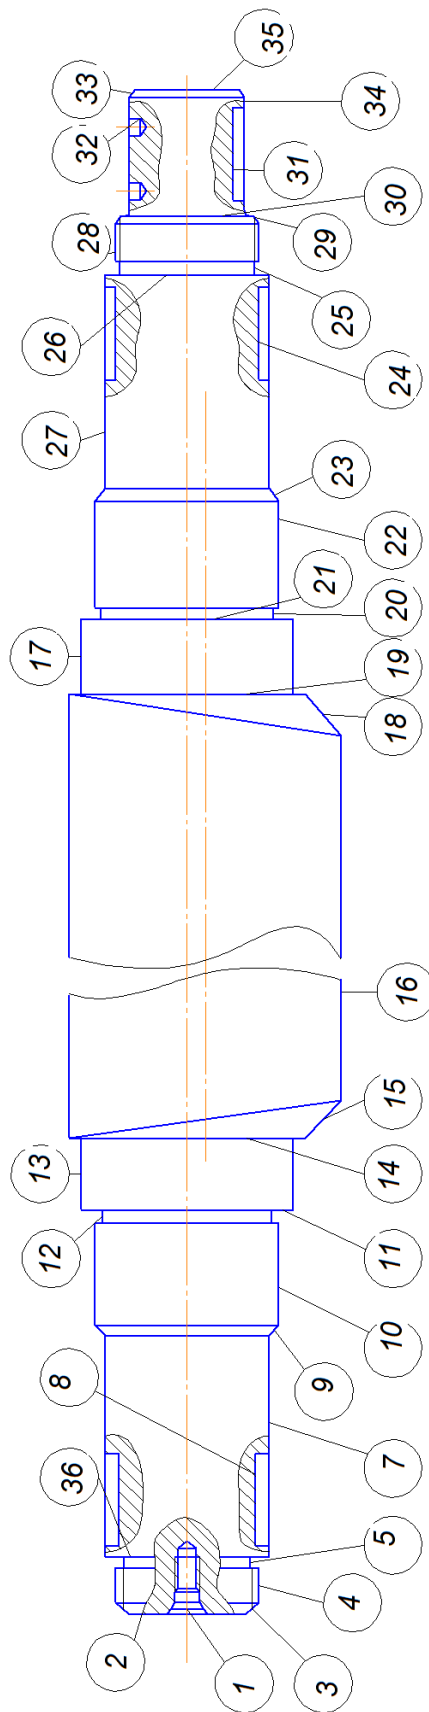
Ескіз деталі "Вал 31214М.03.401" з номерами поверхонь
